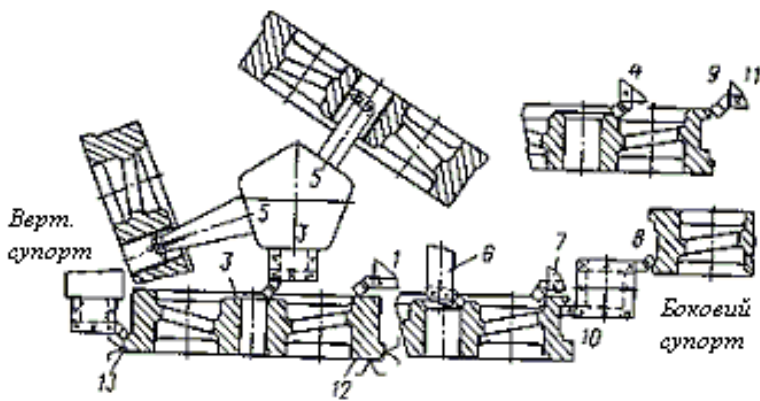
Схема чорнової обробки ходового колеса на токарно-карусельному верстаті.
